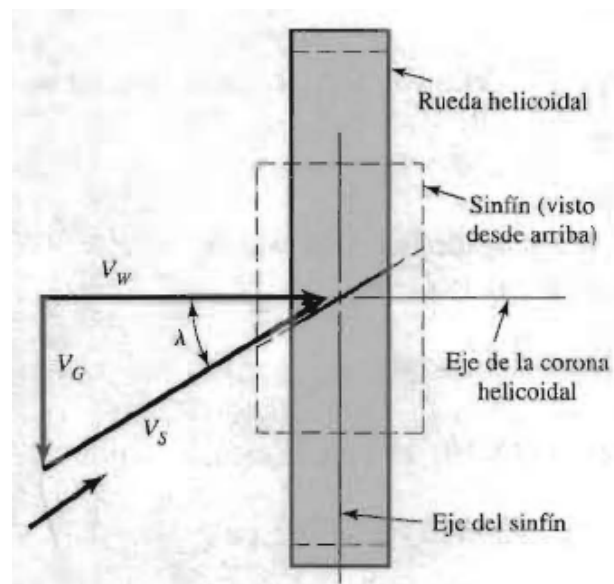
COMPONENTES DE LO VELOCIDAD EN UN ENGRANAJE DE TORNILLO SINFIN.
